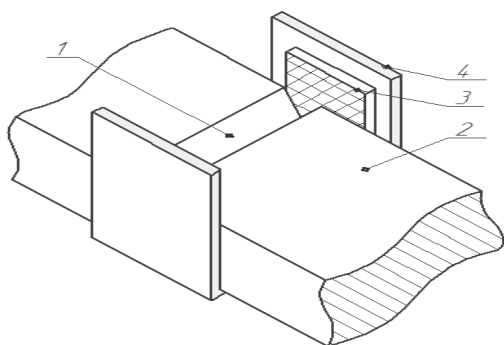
Схема сварки короткого стыкового соединения
